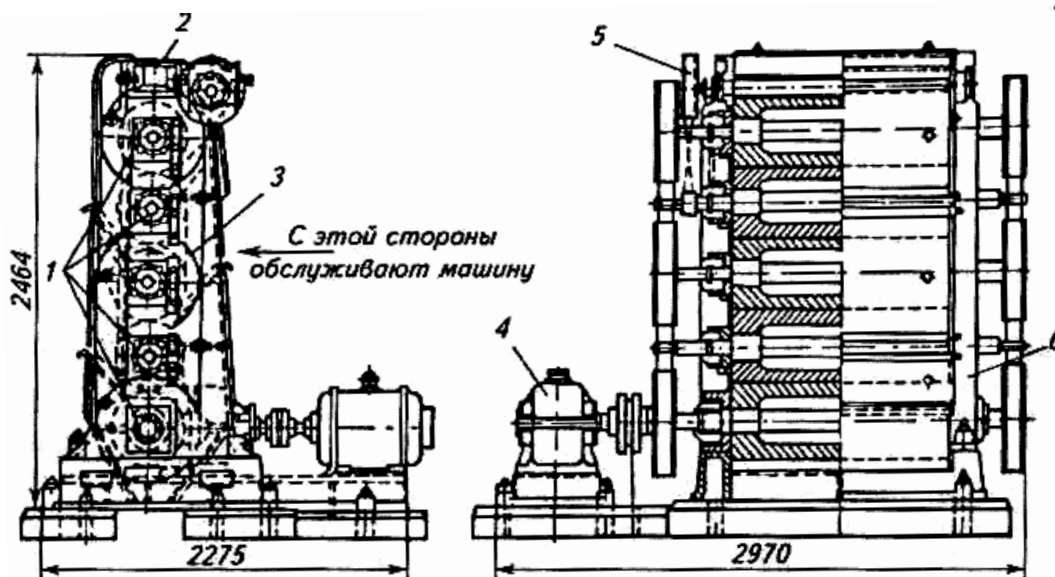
Схема пятивалкового станка типа ВС-5: 1 - корпуса подшипников; 2 — вставки; 3 — валки; 4 — двухступенчатый редуктор; 5 — ось питающего валика; 6 — вертикальные стойки
